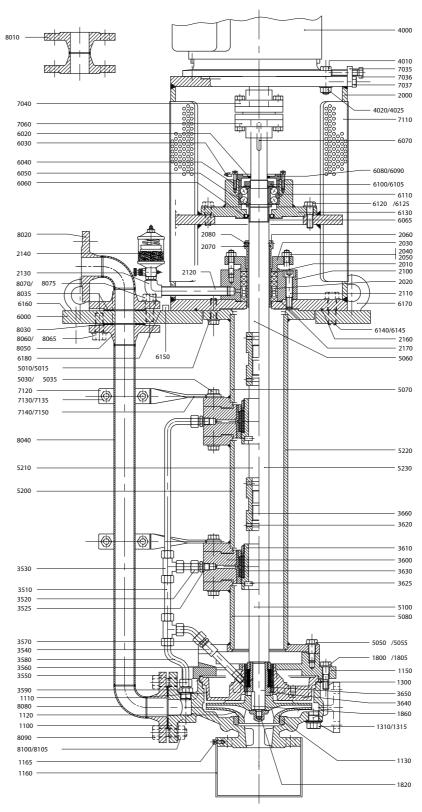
Pompe avec groupe d'étanchéité d'arbre S3.
